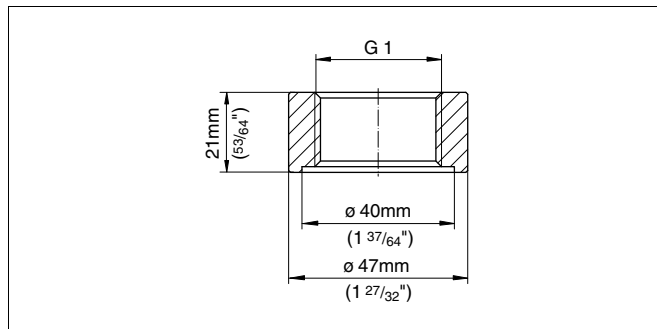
Maße Einschweißstutzen G1 A nach ISO 228-1
